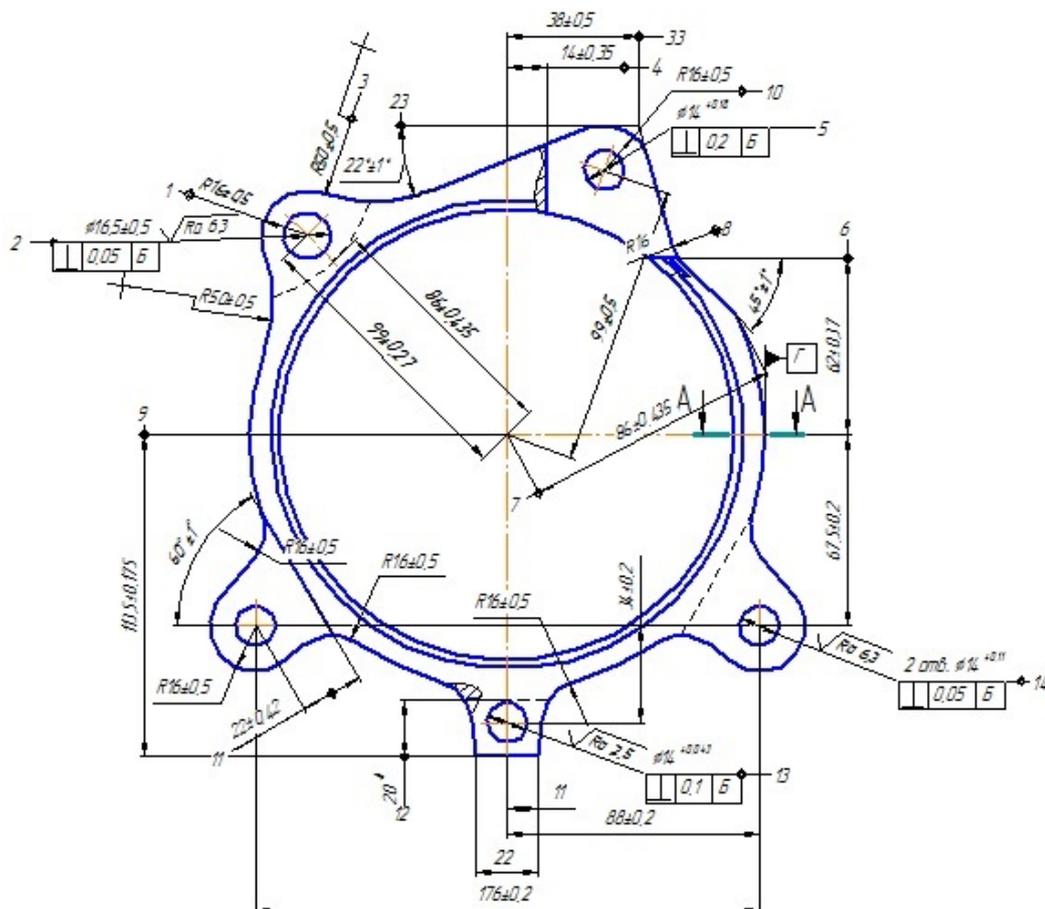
Нумерация обрабатываемых поверхностей детали
